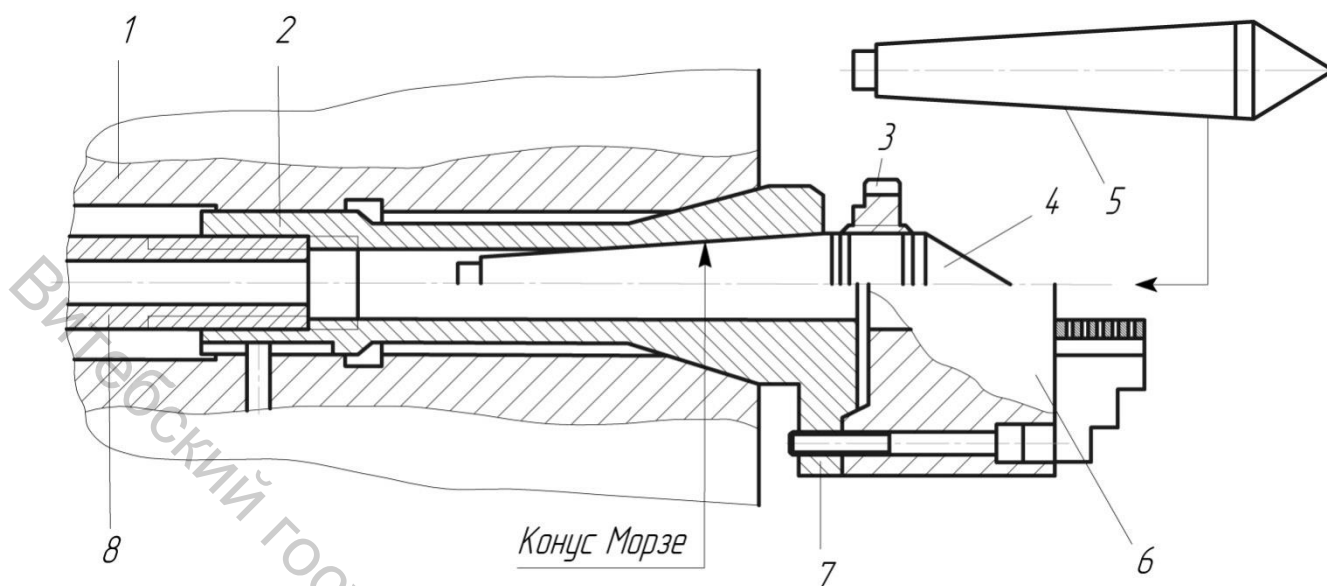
Шпиндель универсального круглошлифовального станка с переходной втулкой для центров и переходной оправкой для кулачкового патрона
